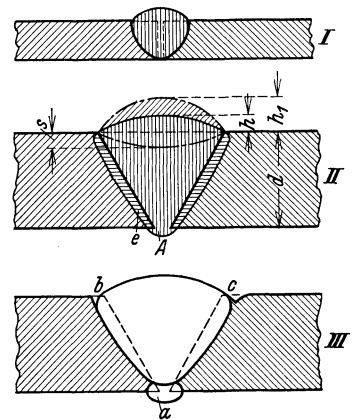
Querschnitte von I- und V-Schweißungen.
